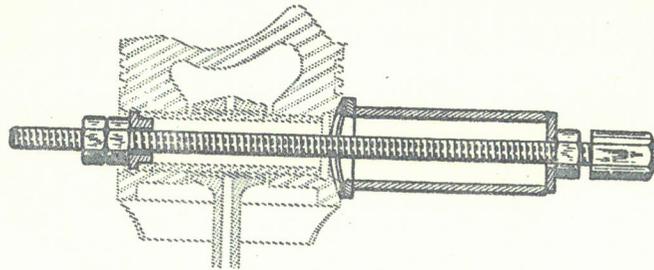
Ausbau der Buchse für Kolbenbolzen
